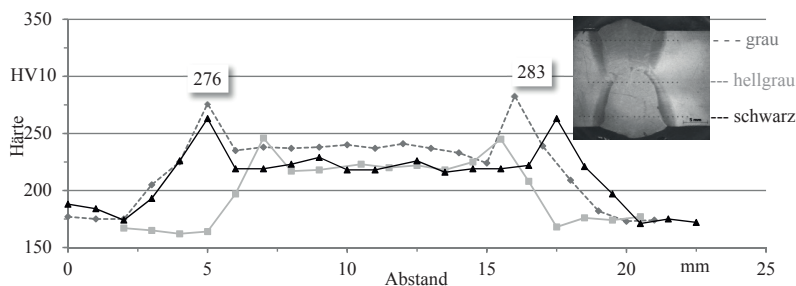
Härte einer Schweißung in Lage/Gegenlage-Technik;  $E = 23 \text{ kJ}\cdot\text{cm}^{-1}$
